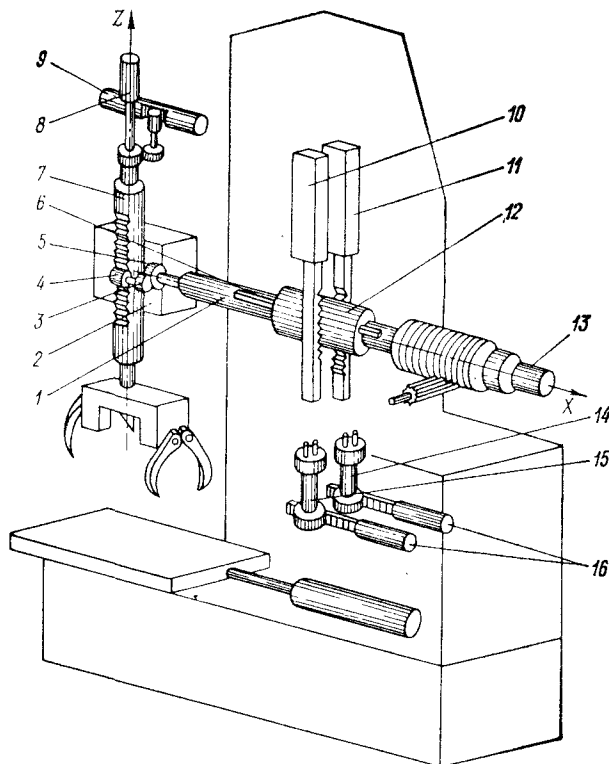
Кинематическая схема робота СМ40Ц4301
